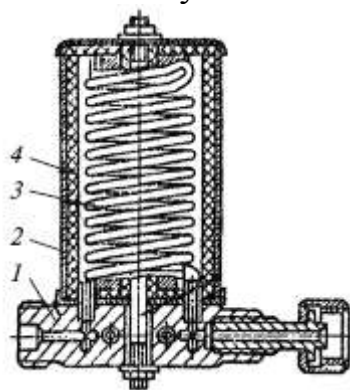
Подогреватель углекислого газа: 1 – корпус; 2 – кожух; 3 – трубка-змеевик; 4 – теплоизоляционный слой; 5 – нагревательный элемент; 6 – накидная гайка
